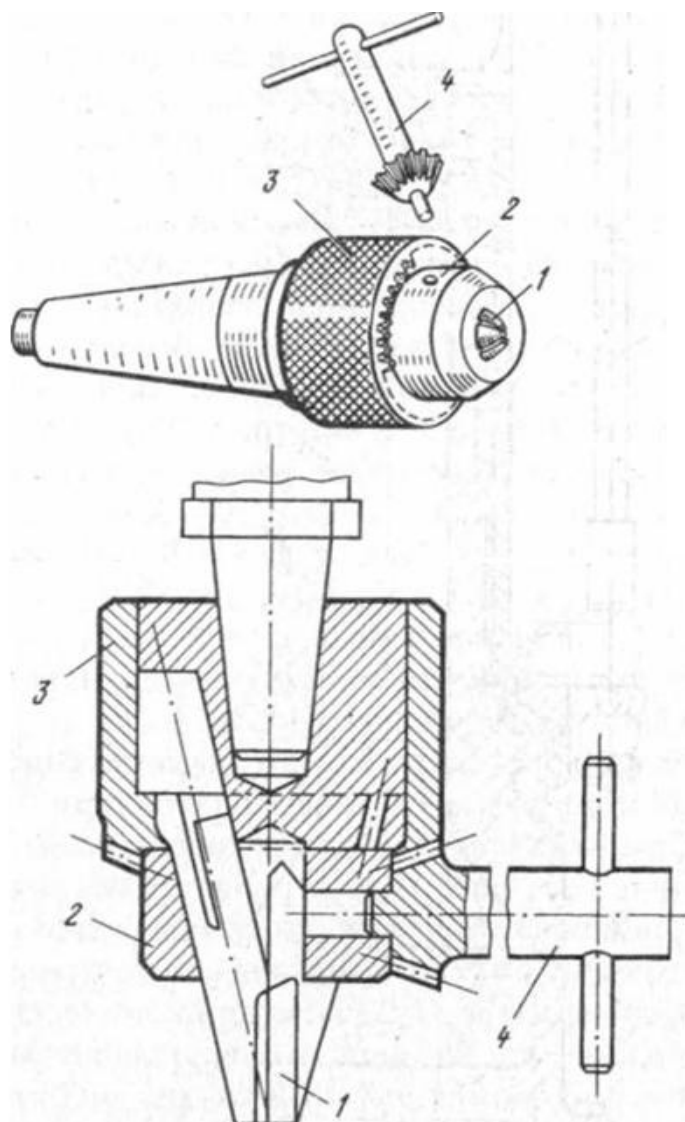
Трехкулачковый сверлильный патрон.
